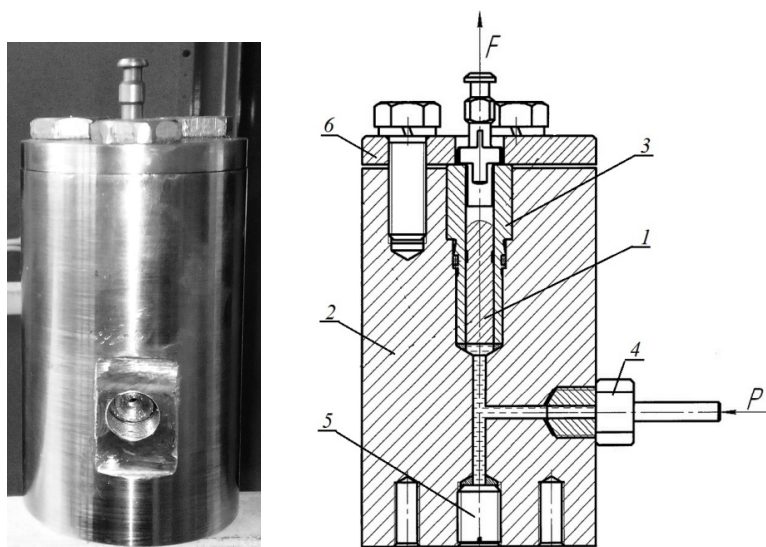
Основной блок регулятора: 1 – плунжер; 2 – корпус регулятора; 3 – корпус плунжера; 4 – штуцер; 5 – заглушка; 6 – крышка корпуса регулятора
